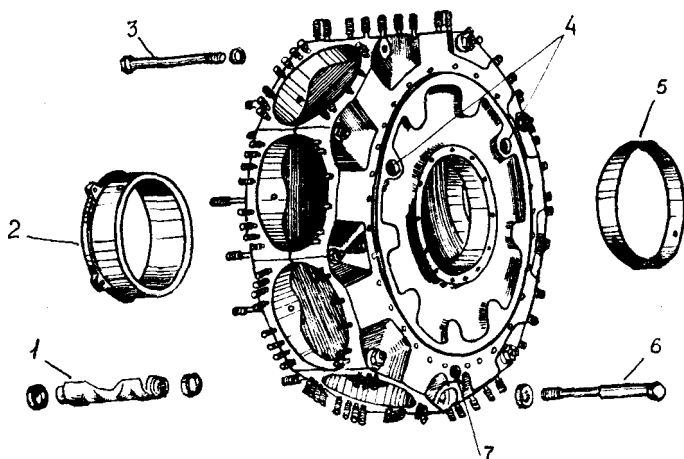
Средний картер: 1—дефлектор; 2—гнездо переднего подшипника коленчатого вала; 3—стяжной болт; 4—суфлирующие отверстия; 5—гнездо заднего подшипника коленчатого вала; 6—болт крепления среднего картера и носка картера; 7—гнездо дефлектора
